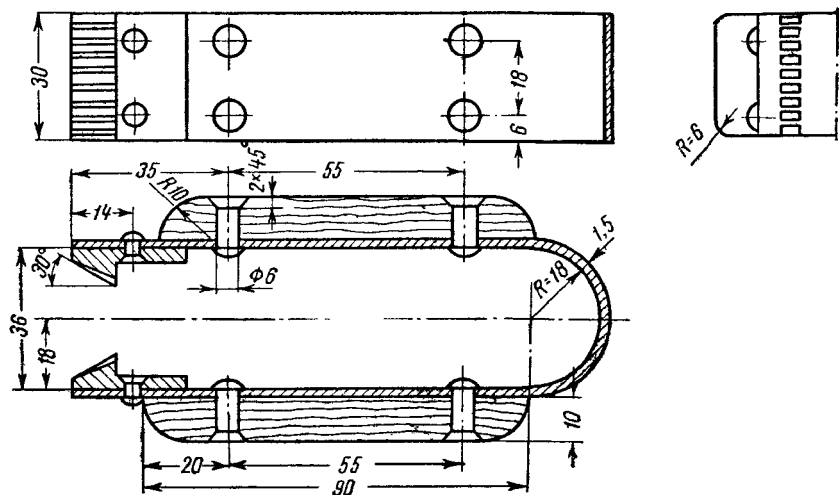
Приспособление для зачистки концов секций (размеры в мм).
